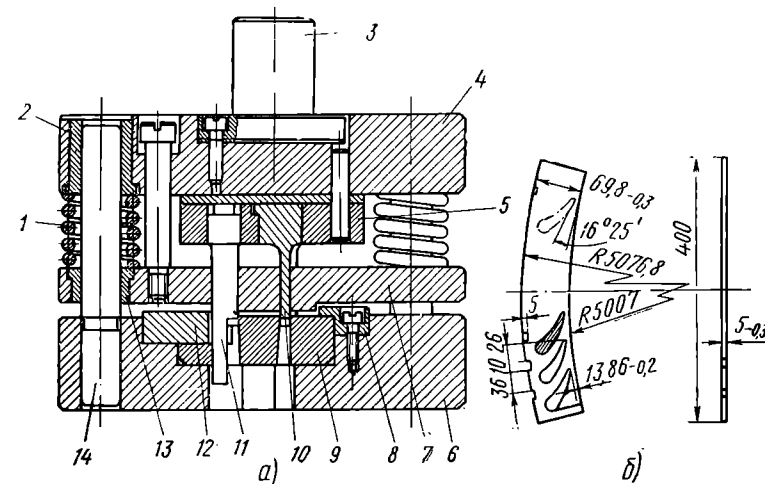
Штамп для пробивки фигурных отверстий и боковых пазов (а) и эскиз детали (б)
